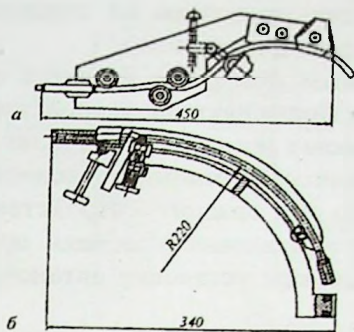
Схемы мундштуков для электрошлаковой сварки
